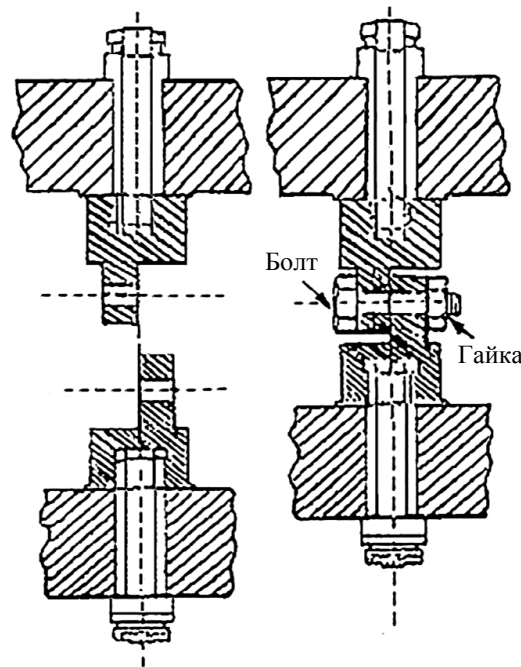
Схема приспособления для испытания на одинарный срез [2]
